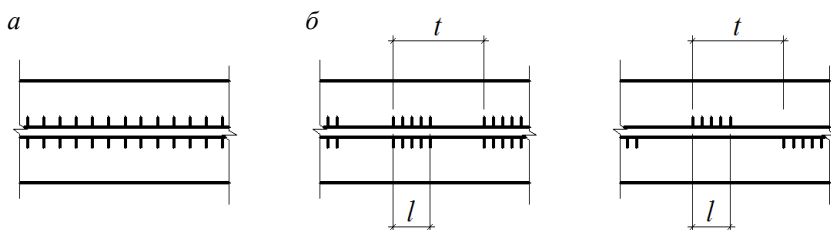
Сварные швы по протяженности:
